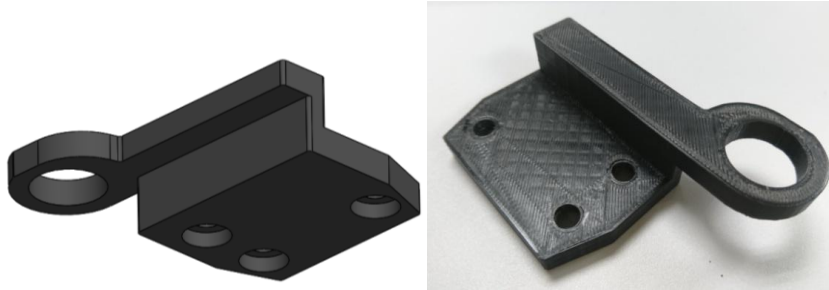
Modelo CAD y pieza final impresa del soporte del sensor.
